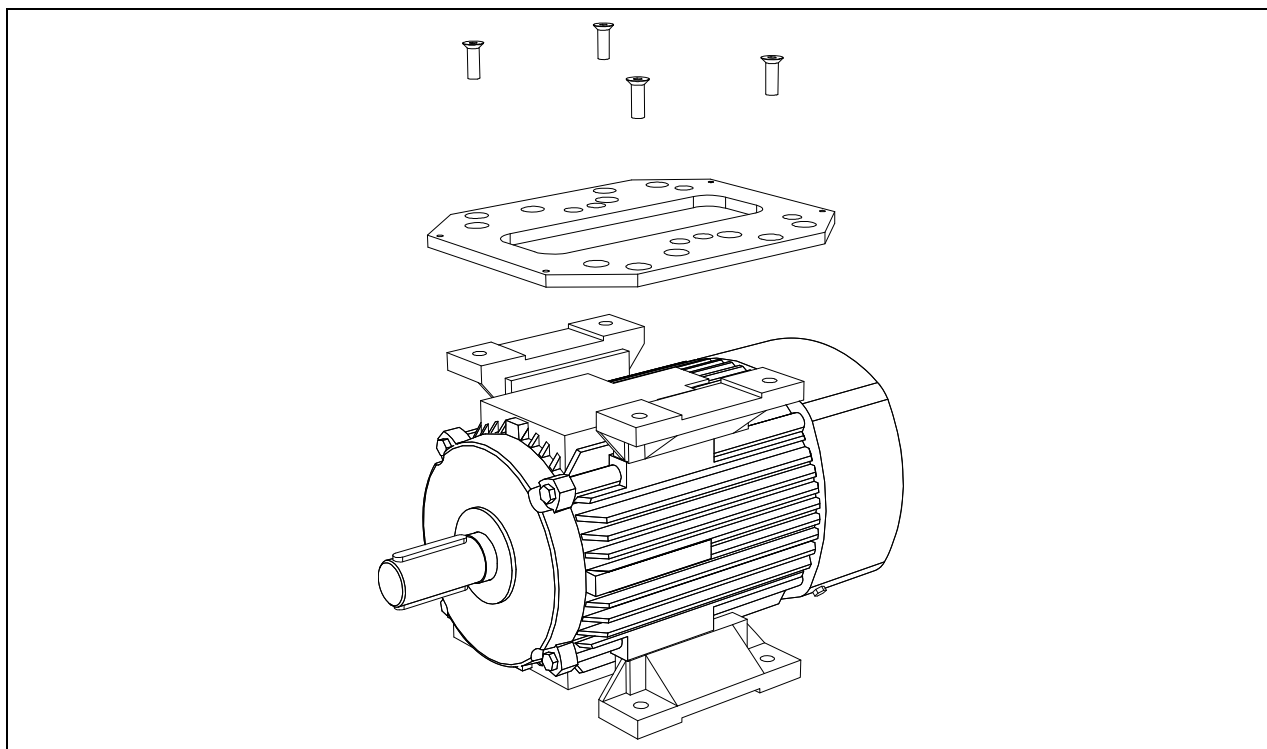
Bringen Sie den Flanschadapter am Motor an.
